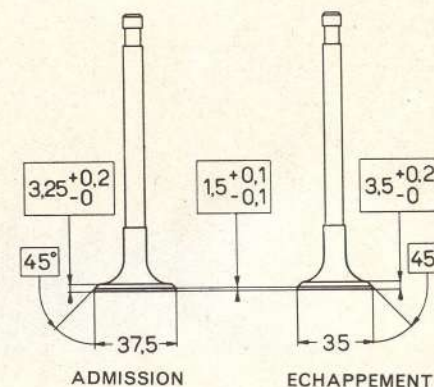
Dimensions et conicité originaires des sièges de soupapes.
